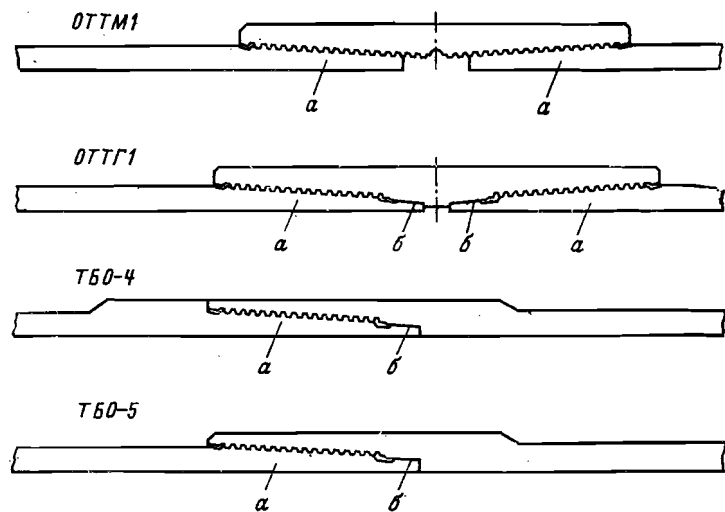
Конструкции соединений труб с трапецидальной резьбой: а — резьба; б — уплотнительная часть соединения
